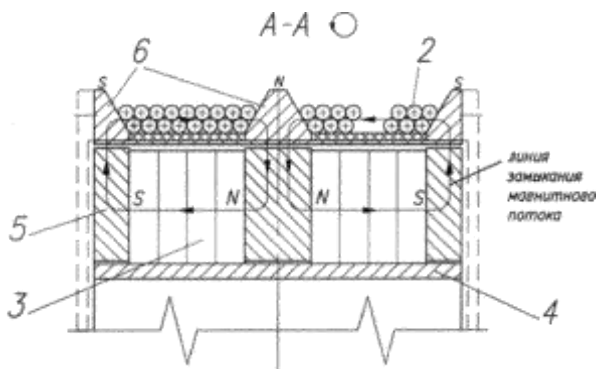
Барабанно-канальный высокоградиентный магнитный сепаратор с высокоэнергетичными постоянными магнитами и ферромагнитной шариковой осадительной поверхностью: 1 – несущий неподвижный вал; 2 – ферромагнитная шариковая рабочая зона; 3 – высокоэнергетичные постоянные магниты; 4 – ярмо; 5 – элементы магнитопровода; 6 – полюсные наконечники; 7 – регенерационный грохот
